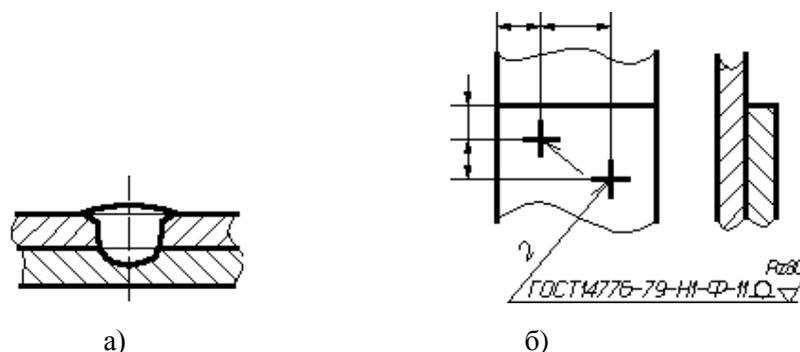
Одиночные сварные точки соединения внахлестку, выполненные дуговой сваркой под флюсом: а) форма поперечного сечения шва; б) с лицевой стороны
